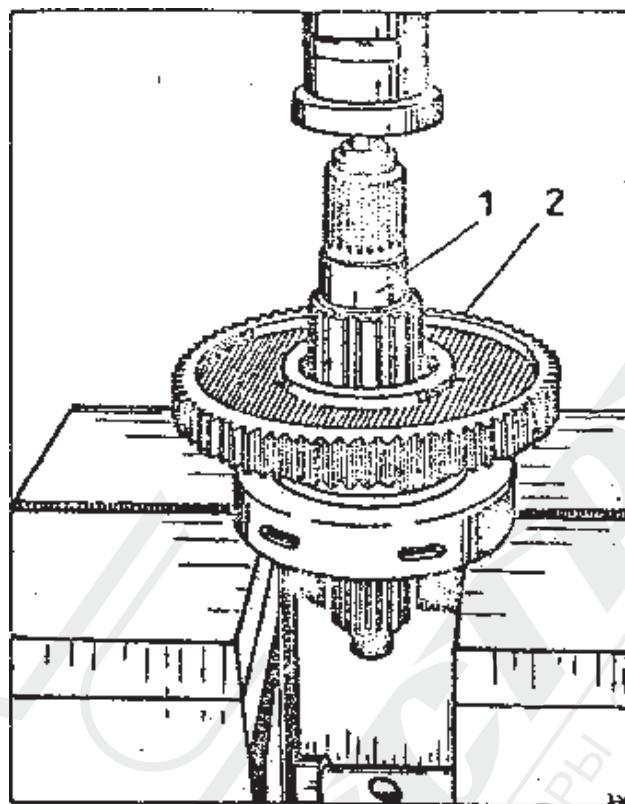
Выдавливание подшипников со ступицы зубчатого колеса /обратная установка - вдавливание, подшипников/ /1,2 - см. на рис. 2-20/.
